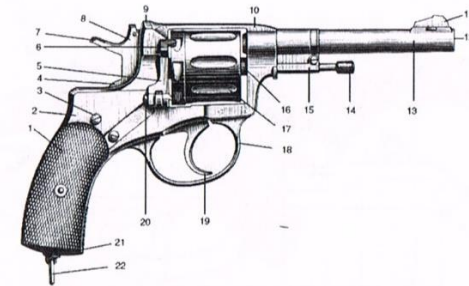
Элементы конструкции револьвера образца 1895 года «Наган»:
